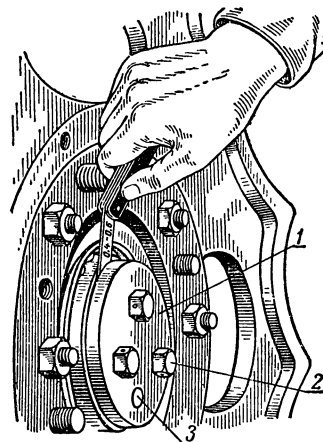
Определение зазора между торцом внутреннего кольца подшипника и шайбой.
